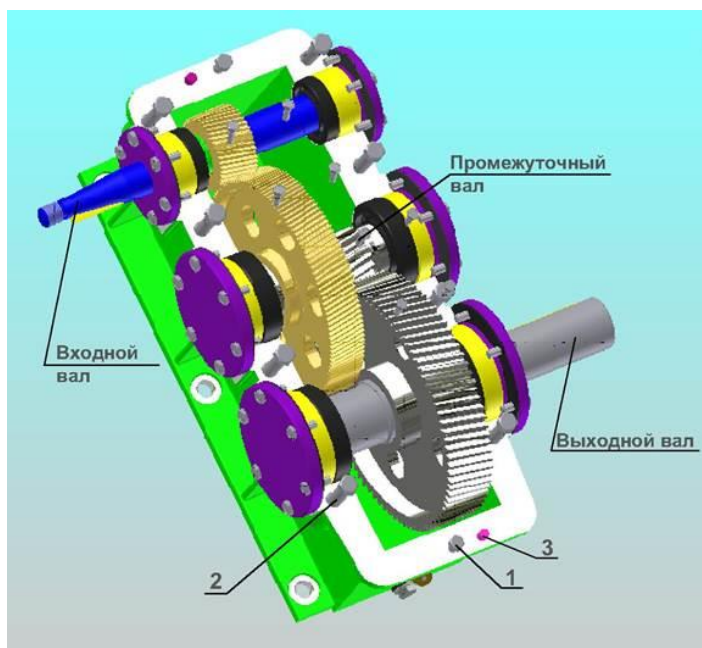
Редуктор зубчатый цилиндрический двухступенчатый без крышки
